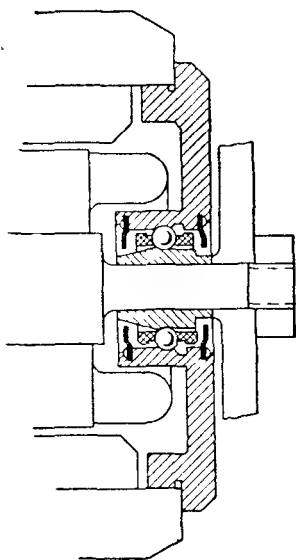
Подшипник ГД с маслозащитными шайбами и канавкой на наружном кольце для сохранения смазки
